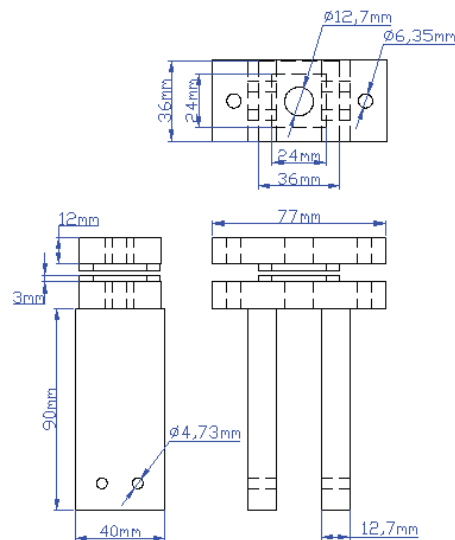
Diseño de los soportes para el montaje de la muestra
